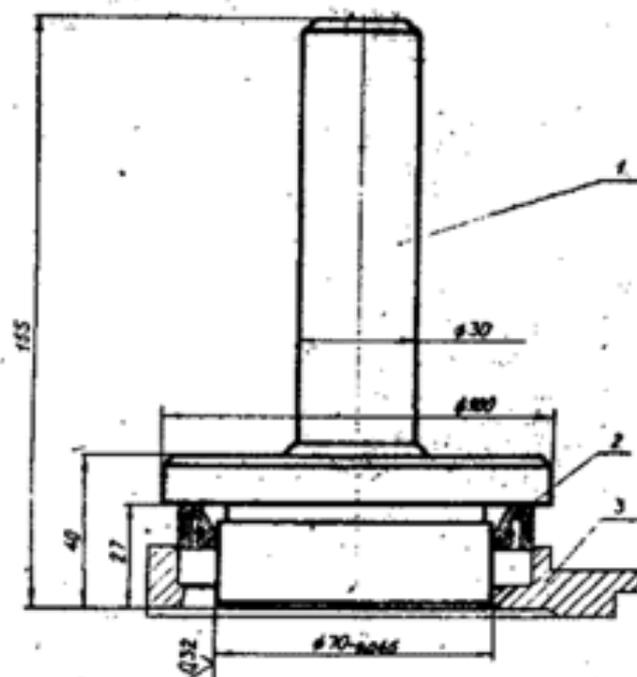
Запрессовка манжеты в держатель заднего подшипника коленчатого вала: 1 - оправка М9840-880; 2 - манжета; 3 - держатель
